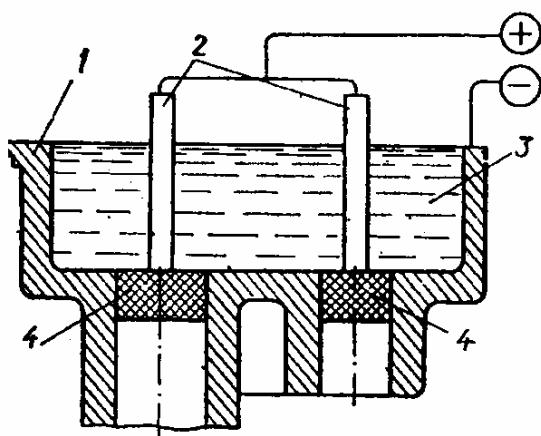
Схема електролітичного нарощування внутрішньої поверхні корпуса насоса:
